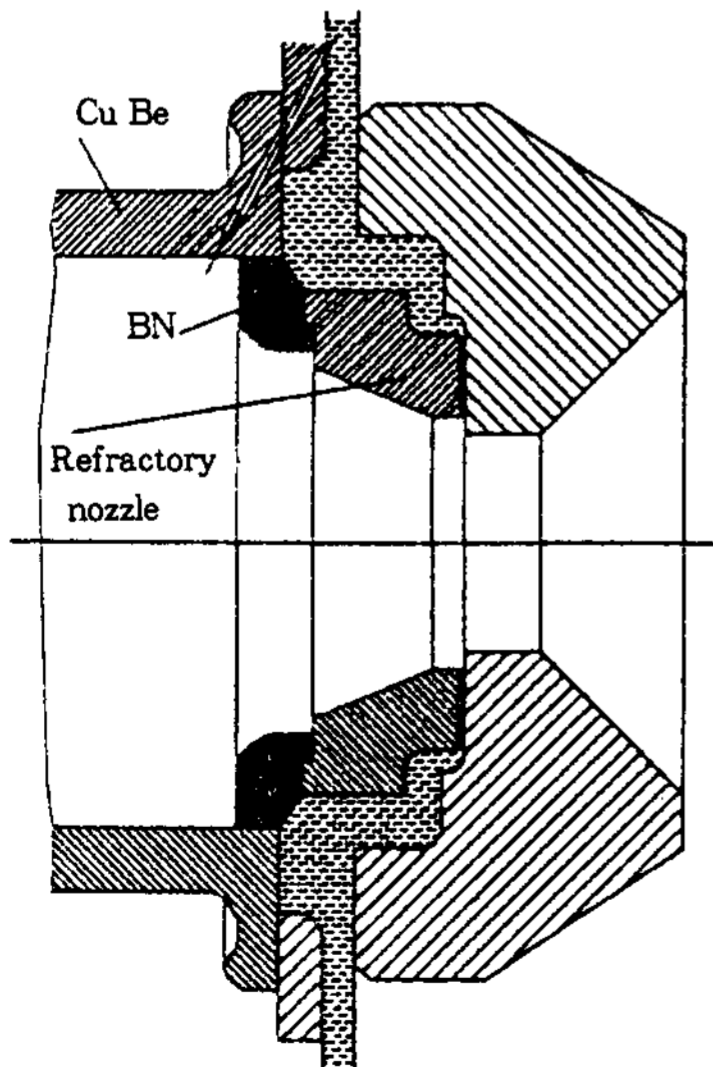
강의 수평연속주조를 위한 tundish와 mould의 연결구조
